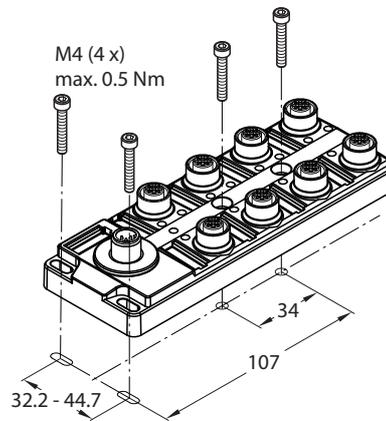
Befestigung des Geräts auf einer Montageplatte
